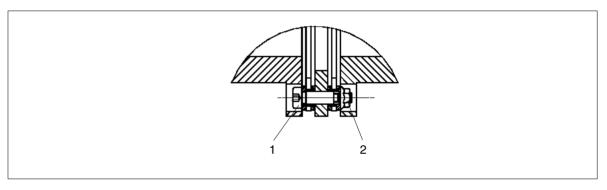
Vue détaillée de la vis d'ajustage à épaulement et de l'écrou à collet
